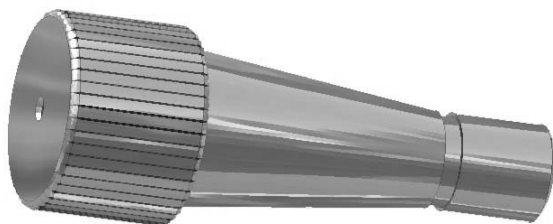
Эталонная оправка для настройки осевого инструмента
